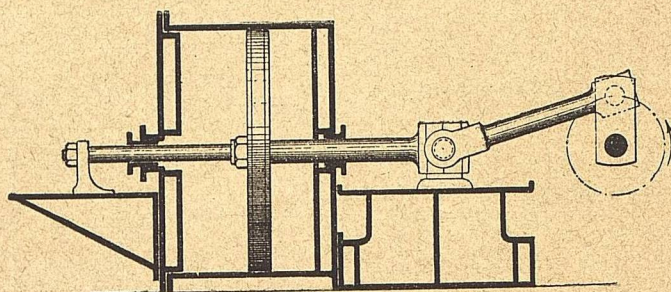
MÁQUINA DE BARRA DIRECTA
